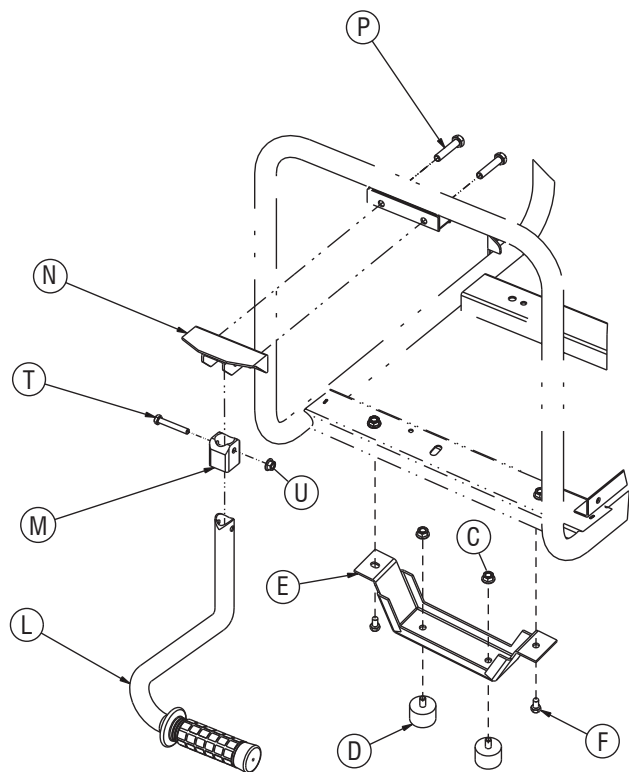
С. Сборка ножи (GP5000/GP6000)
